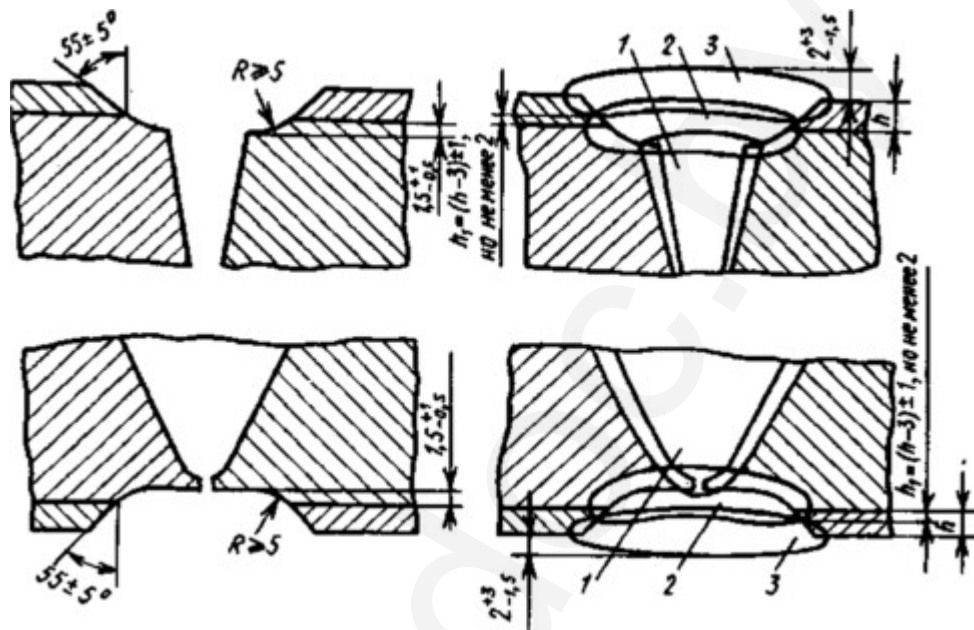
Схема разделки и выполнения сварных соединений деталей из двухслойных сталей:
